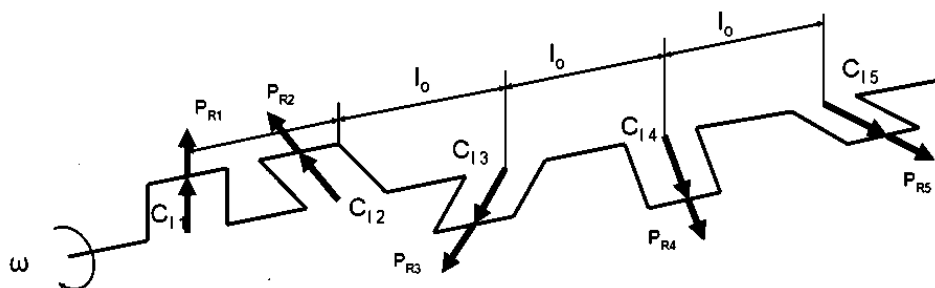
Схема коленчатого вала и расположения векторов центробежных сил инерции двигателя 10V144°
